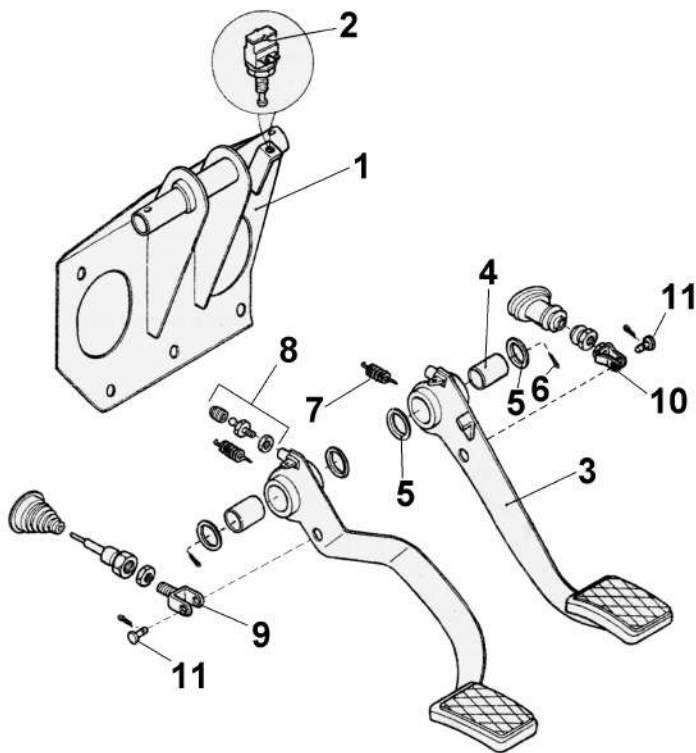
7 Детали кронштейна педалей сцепления и тормоза: 1- кронштейн; 2- выключатель сигнала торможения; 3- педаль тормоза; 4- втулка; 5- шайба; 6- шплинт; 7- возвратная пружина; 8- ограничительный болт; 9, 10- вилки; 11- палец со шплинтом
